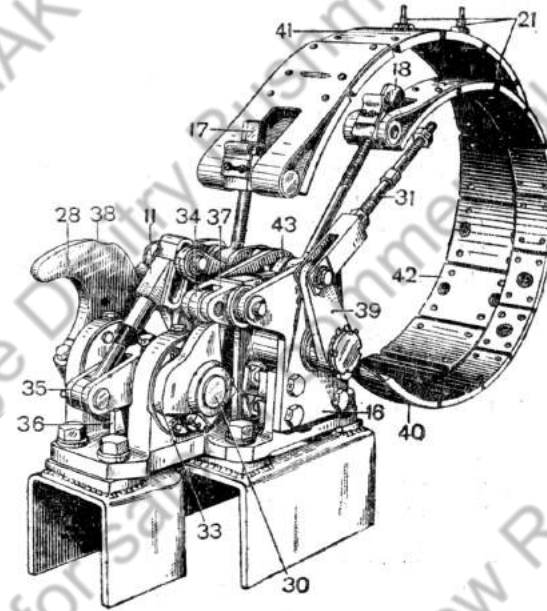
Тормозной мостик с тормозными лентами: 11 — тяга с проушиной; 16 — кронштейн; 17 и 18 — регулировочные гайки; 21 — регулировочные гайки; 28 — кулачок-разделитель; 30 — передний вал; 33 — профильный кулачок; 34 — ролик; 35 — рычаг; 36 — упор; 37 — дульный рычаг; 38 — дунка кулачка-разделителя; 39 — рычаг; 40 — тормозная лента малого тормоза; 41 — тормозная лента остановочного тормоза; 42 — чугунная колодка; 43 — приводной рычаг малого тормоза
